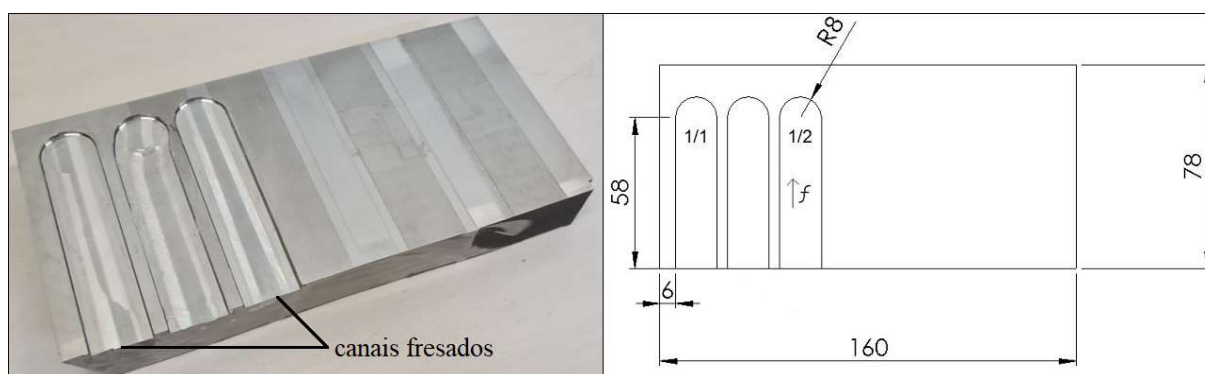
Amostra fresada na condição 1 com dimensões e sentido de avanço da usinagem.
